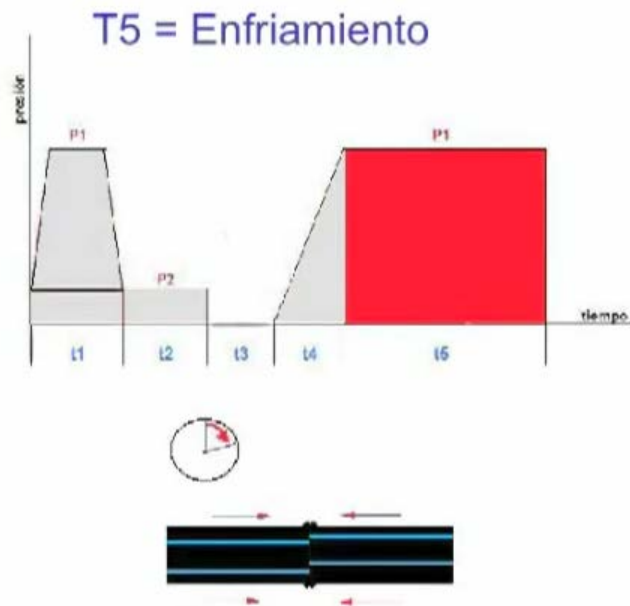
esquema del proceso de soldadura. Enfriamiento.
